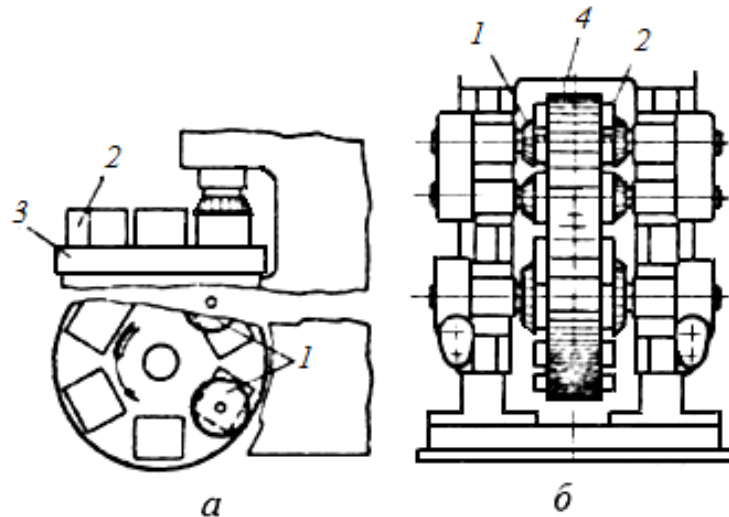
Схеми фрезерних верстатів безперервної дії
